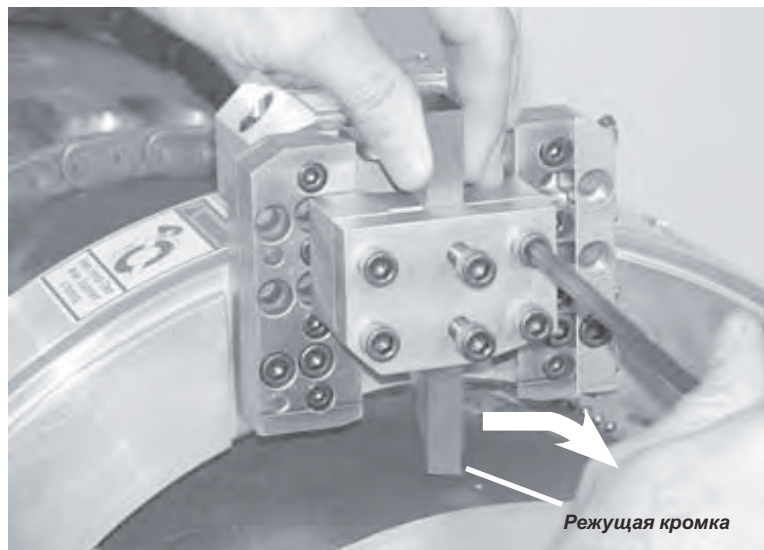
Вставьте резец для снятия фаски в держатель режущей кромкой по направлению вращения.
